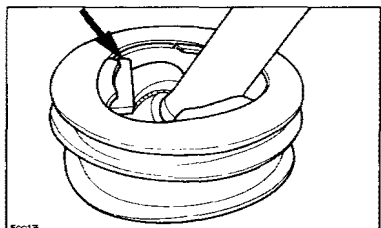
Установите вспомогательную пластину между отогнутой губкой фиксирующей пластины и роликовой обоймой корпуса шарнира
